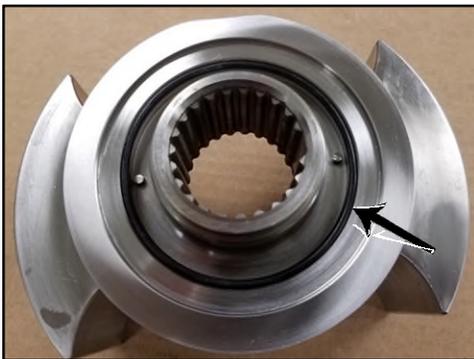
Vorderer Manschetten-O-Ring montiert
